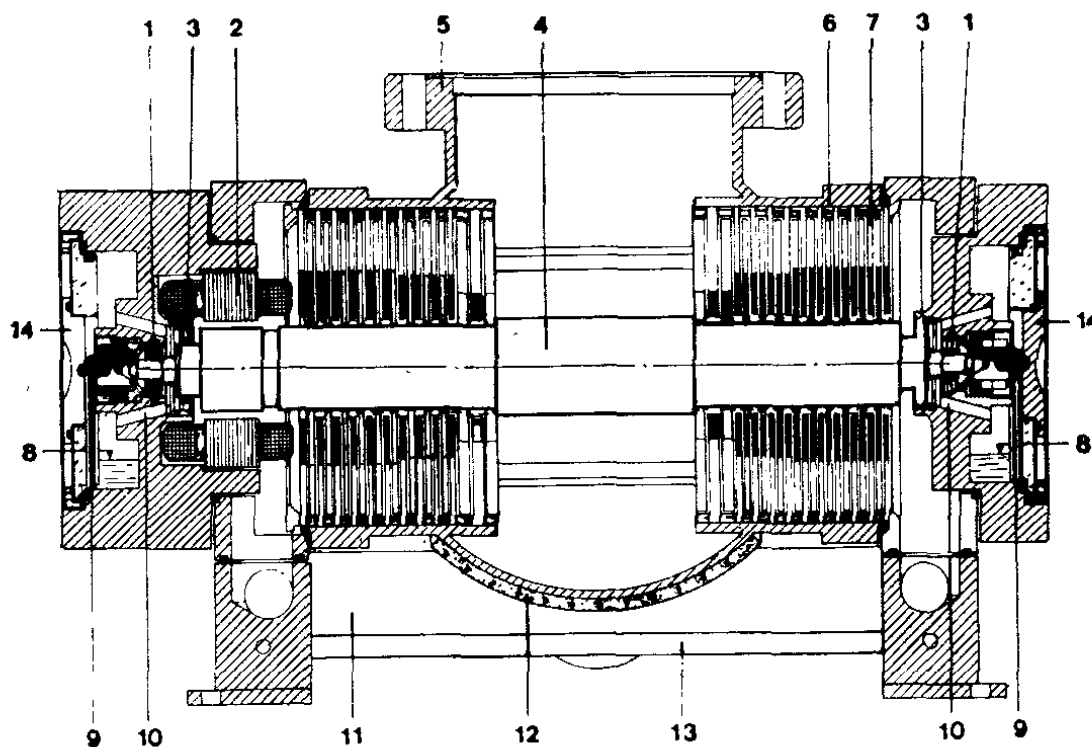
Турбомолекулярный насос фирмы Balzers High Vacuum Ltd. 1 – подшипники; 2 – двигатель; 3 – лабиринтное уплотнение; 4 – вал ротора; 5 – фланец для подсоединения к вакуумной системе; 6 – лопатки ротора; 7 – лопатки статора; 8 – резервуар с маслом; 9 – подача масла в подшипники; 10 – слив масла; 11 – выход (форвакуум); 12 – нагреватель; 13 – водяное охлаждение; 14 – уплотнительная крышка [10, с. 107]
